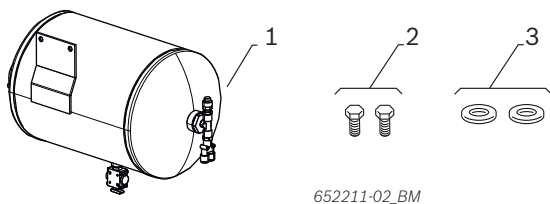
Accesorios para el montaje del recipiente de aire comprimido
